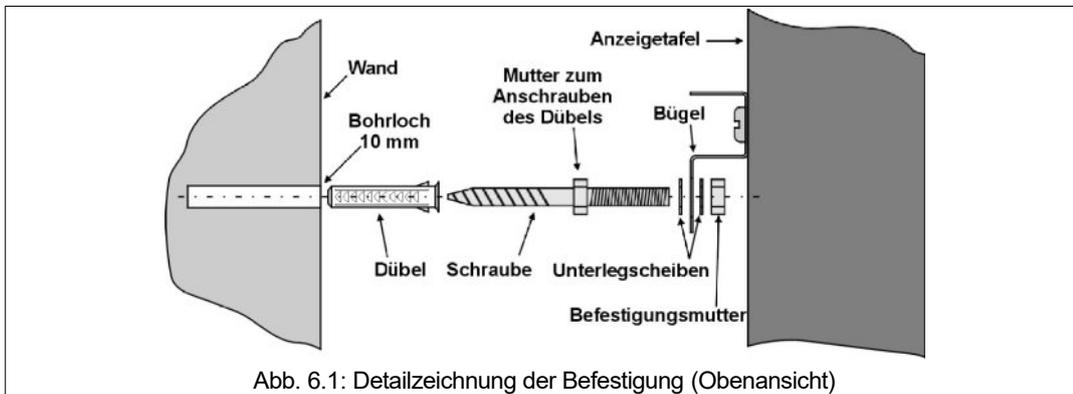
Detailzeichnung der Befestigung (Oberansicht)
